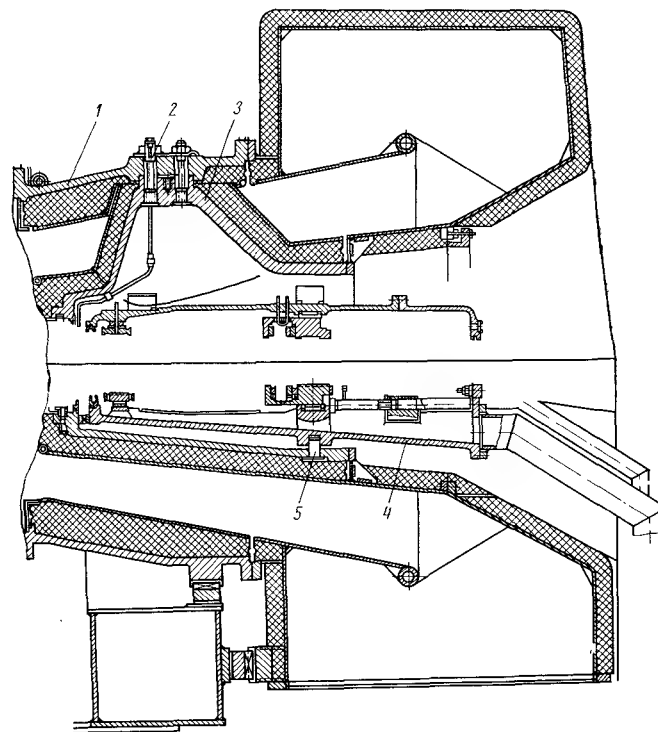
Крепление корпуса подшипника турбины GT-750-6 H3L
